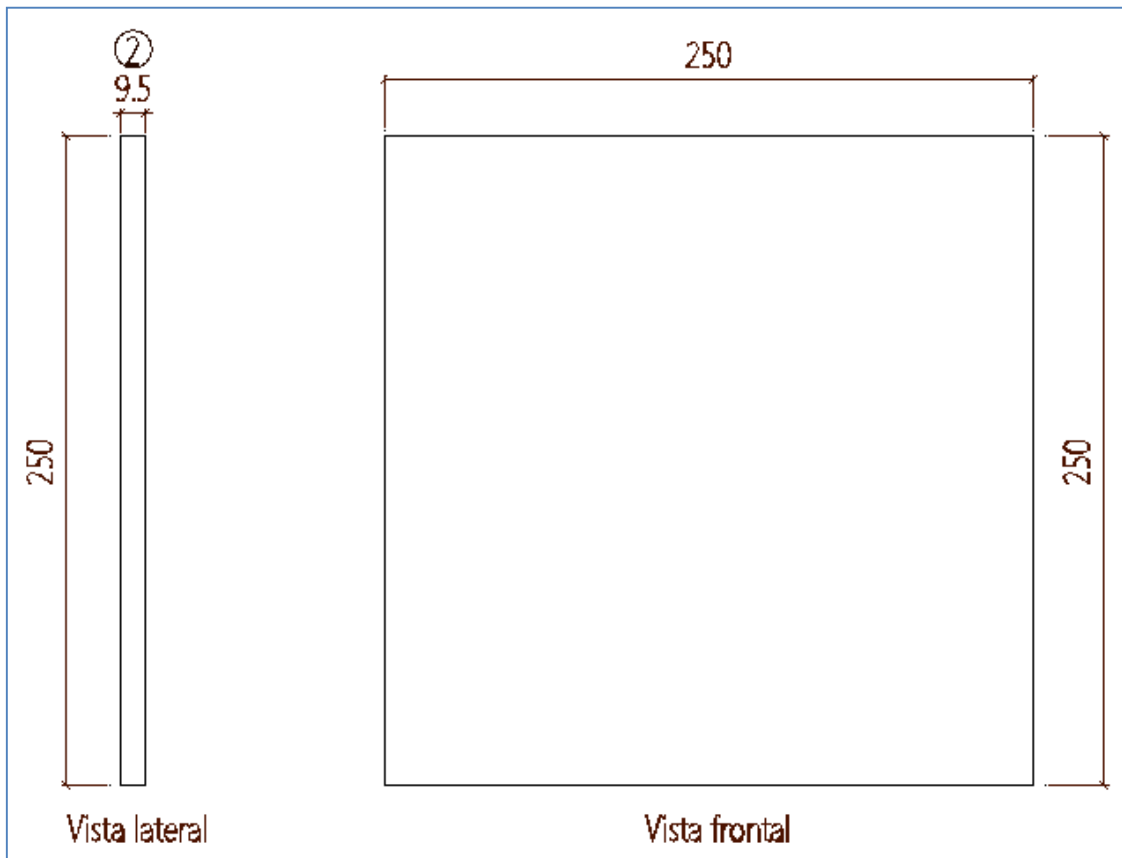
Detalle despiece pieza No.2 modelo 4 tensión.
